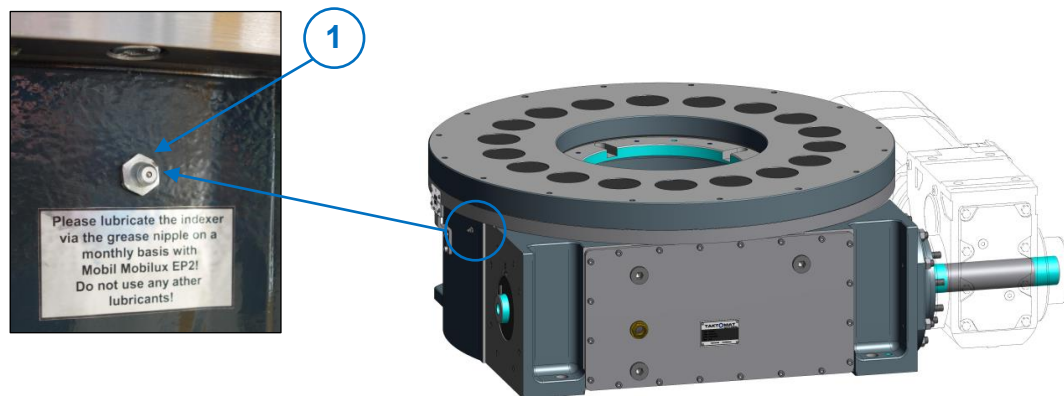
Lubricación de la Indexador rotativo TMF (1) Engrasador
